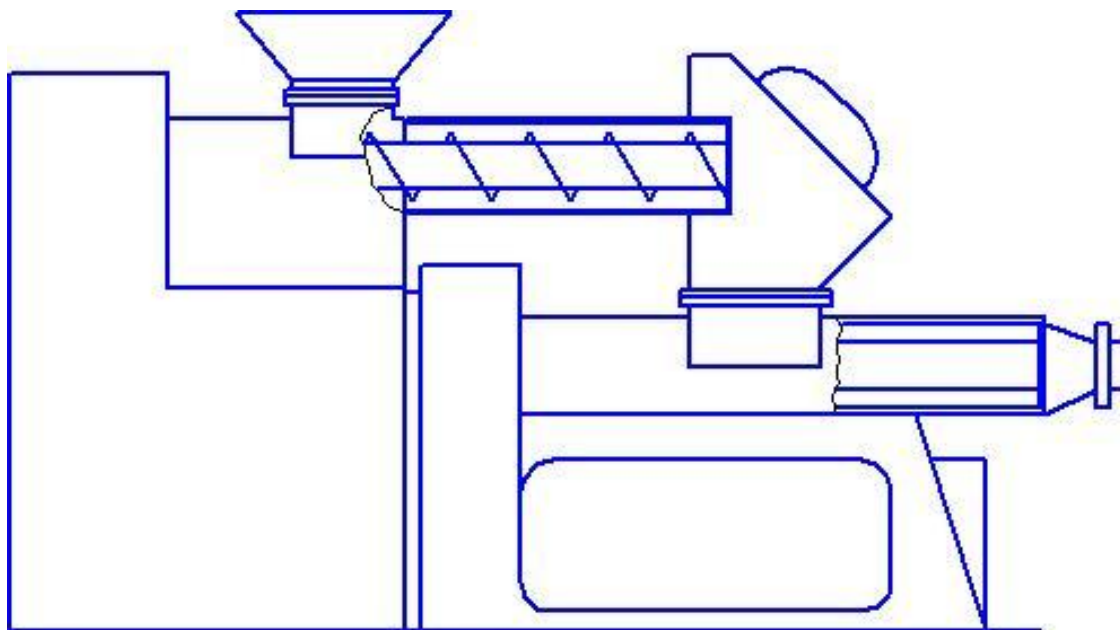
Двухступенчатый одновинтовой пресс
